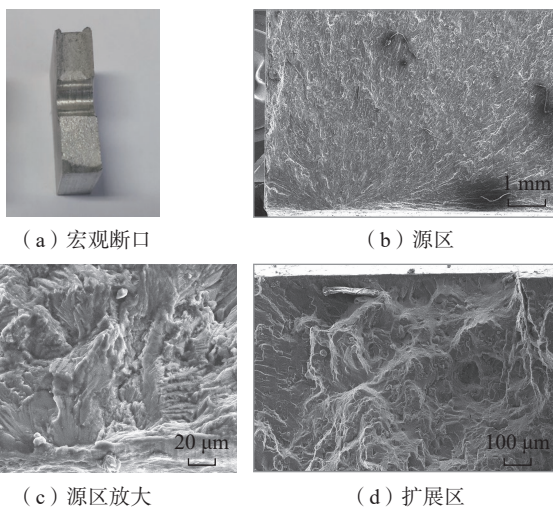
7050 铝合金间隙连接接头疲劳试样微观断口形貌
